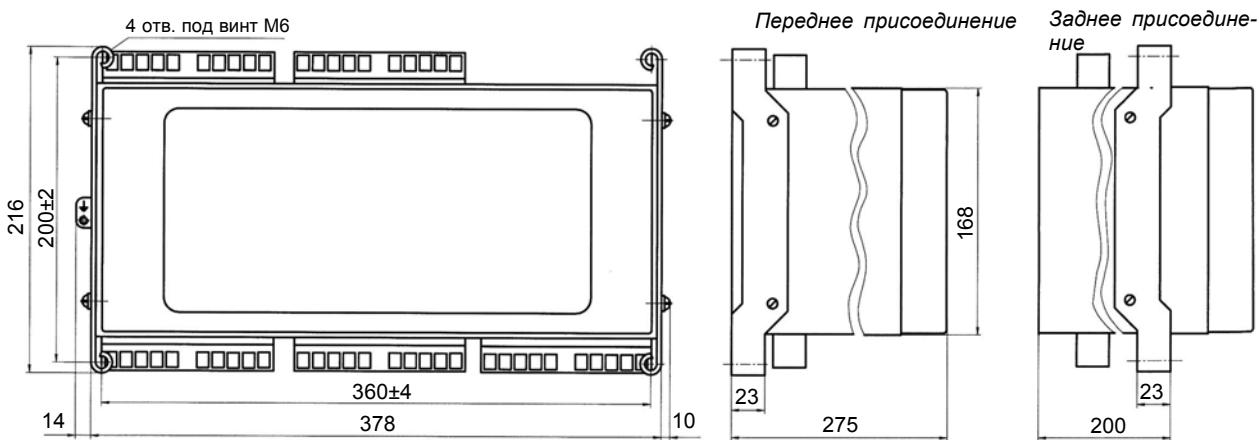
Габаритные, установочные размеры блока типа БЗ 2603
